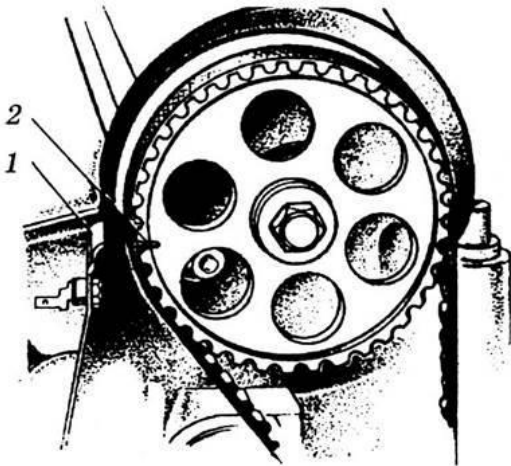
Проверка совпадения меток на звездочке распределительного вала и корпусе подшипников:
